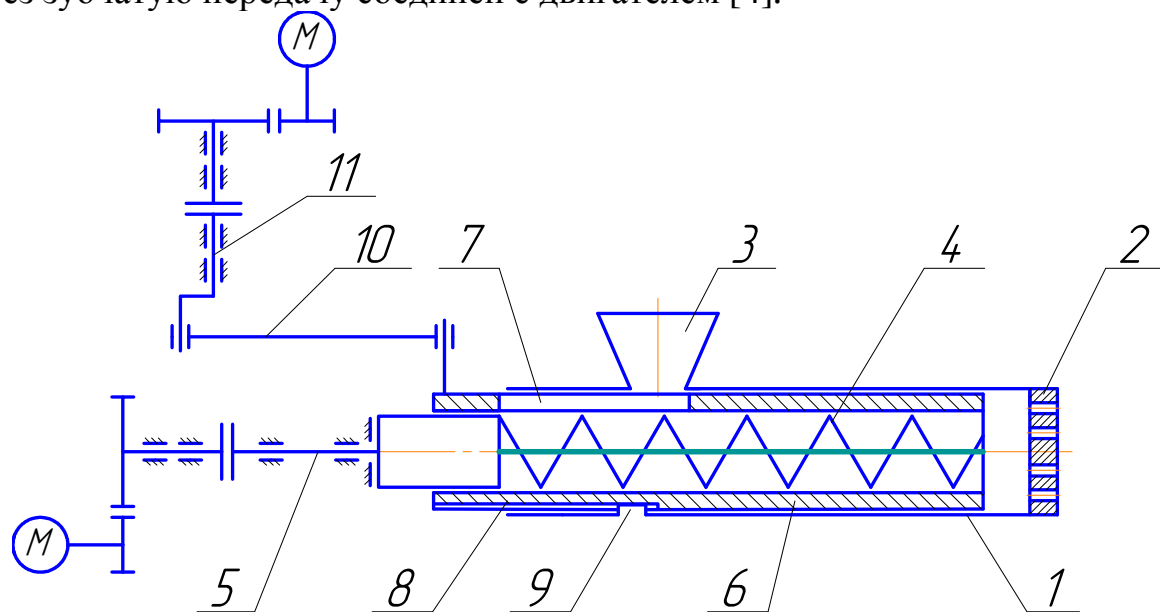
Пресс-экструдер с ползуном кривошипно-ползунного механизма в
